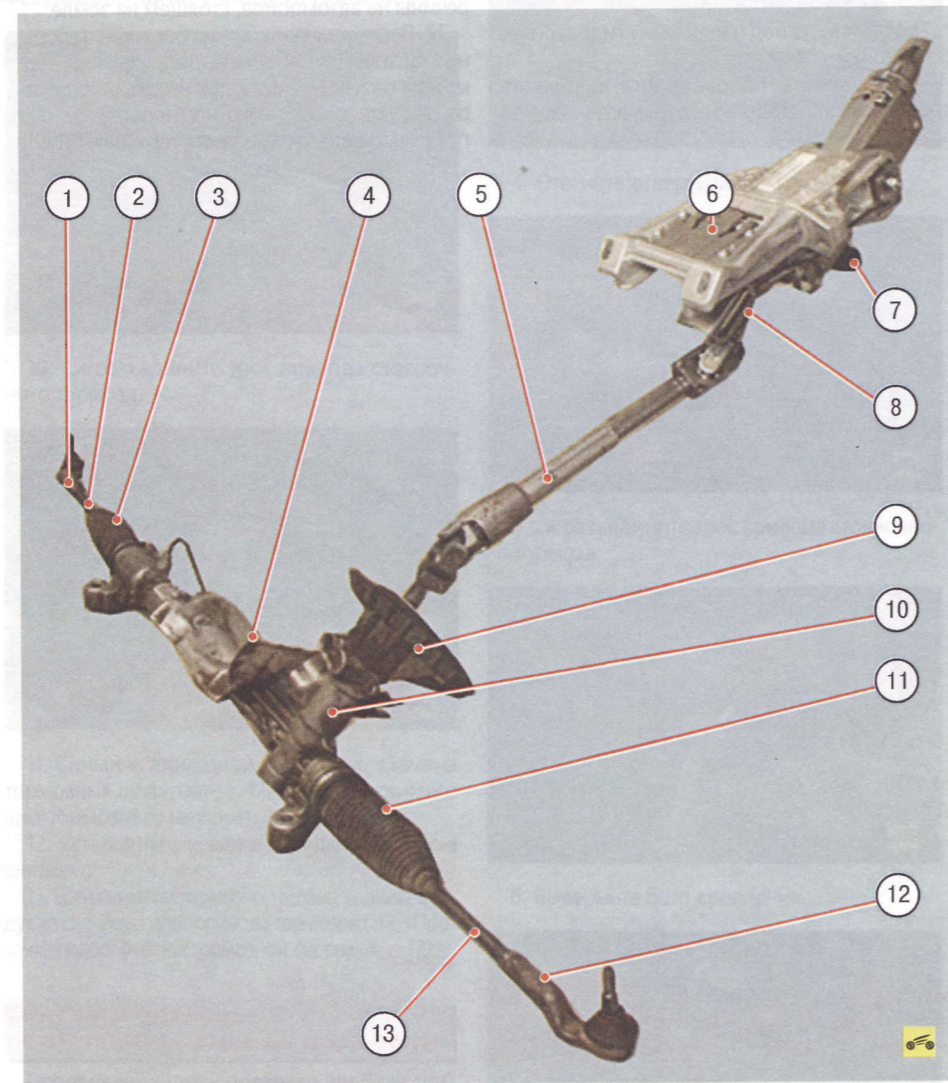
Рулевой механизм с гидроусилителем: 1 – наконечник рулевой тяги (правый); 2 – левая рулевая тяга; 3, 11 – защитные чехлы; 4 – термозакан; 5 – рулевой вал; 6 – рулевая колонка; 7 – рычаг блокировки положения рулевой колонки; 8 – рулевой вал; 9 – уплотнительный чехол; 10 – картер рулевого механизма; 12 – наконечник рулевой тяги (левый); 13 – правая рулевая тяга
